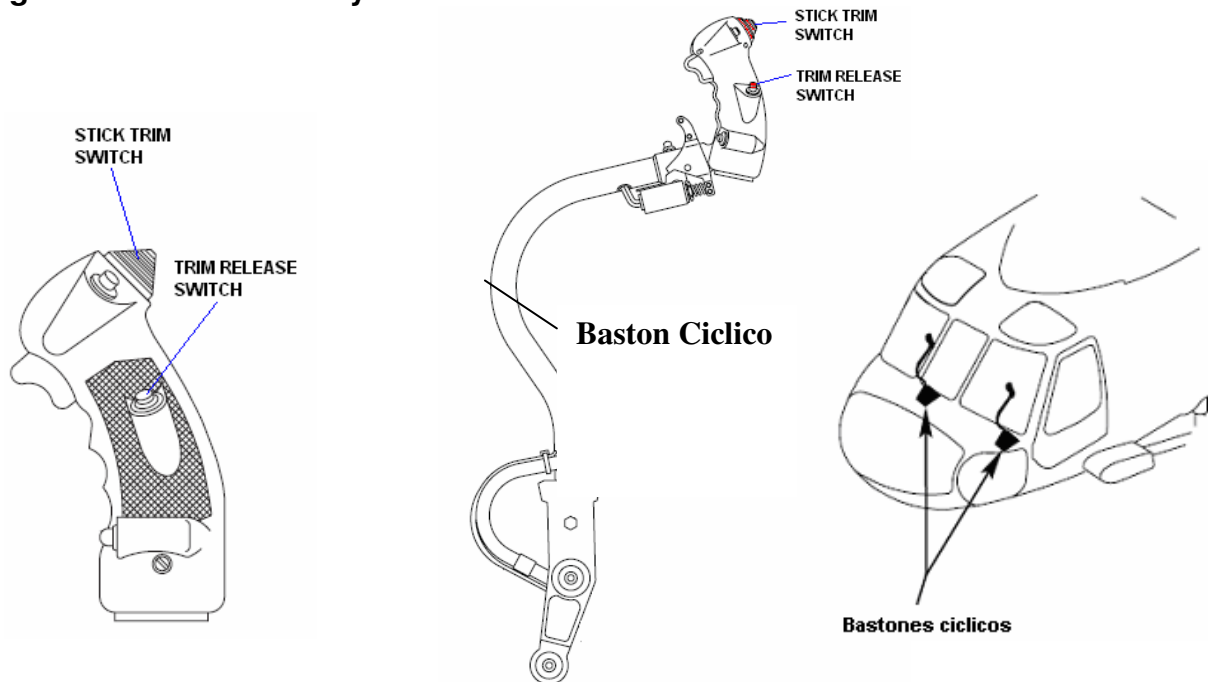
Esquema operacional del PITCH TRIM ASSEMBLY.
